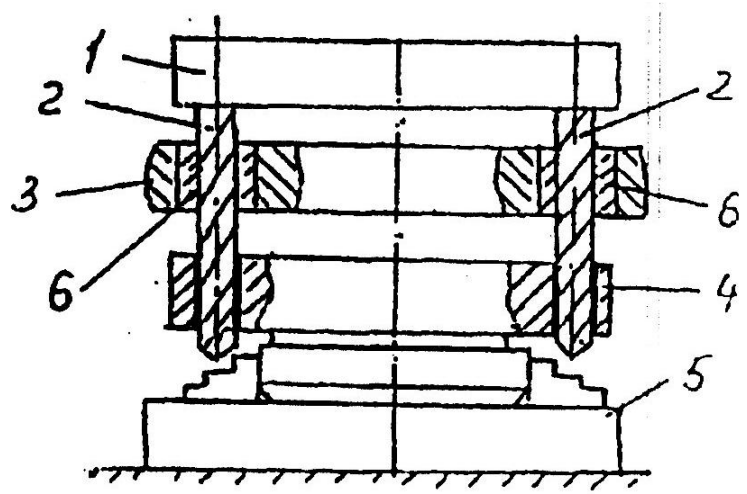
Схема обработки на 045-й сверлильной операции: 1 – многошпindleльная головка; 2 – сверл; 3 – кондукторная плита; 4 – заготовка; 5 – трехлачковый самоцентрирующийся патрон; 6 – кондукторная втулка
